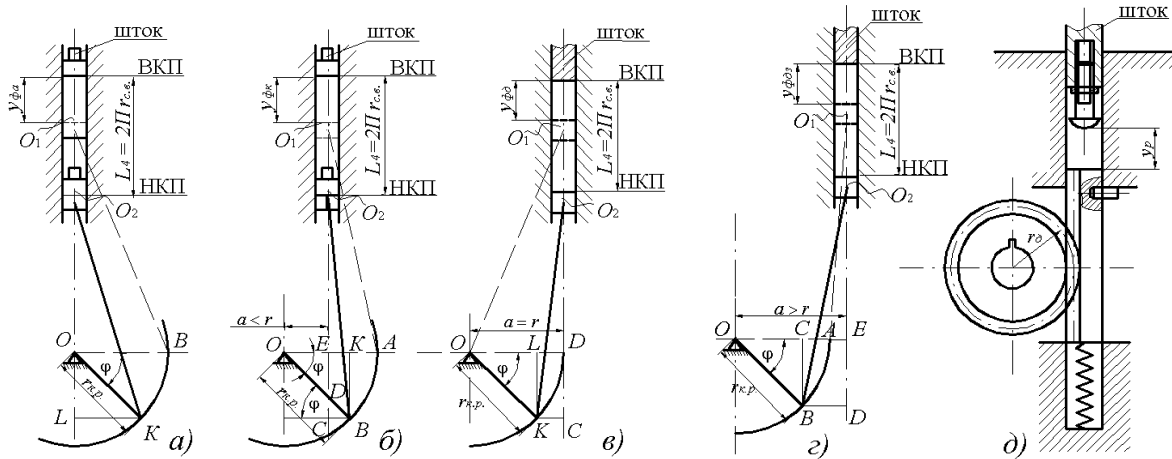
Розрахункові схеми для визначення налагоджуваного розміру у:
